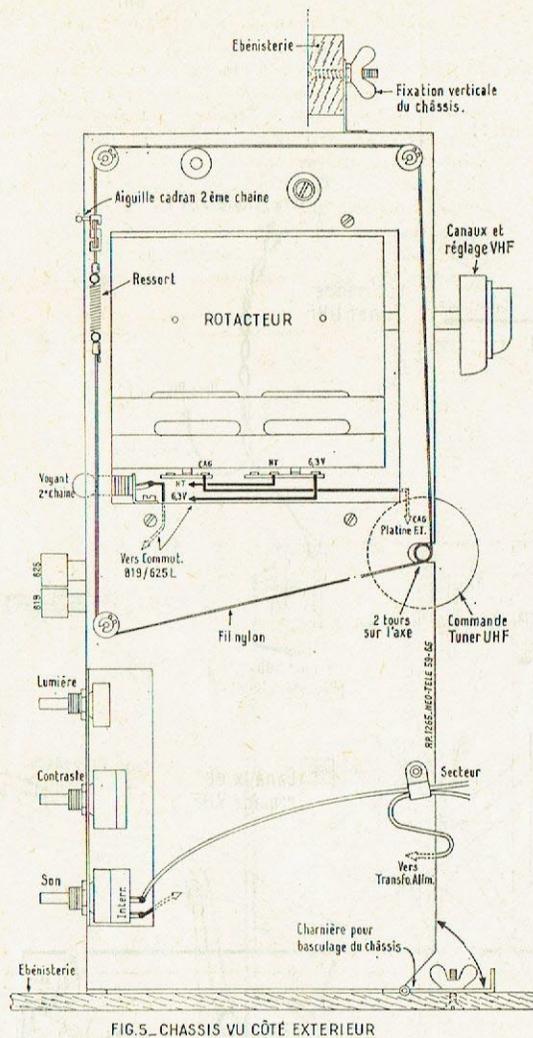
CHASSIS VU CÔTÉ EXTERIEUR
